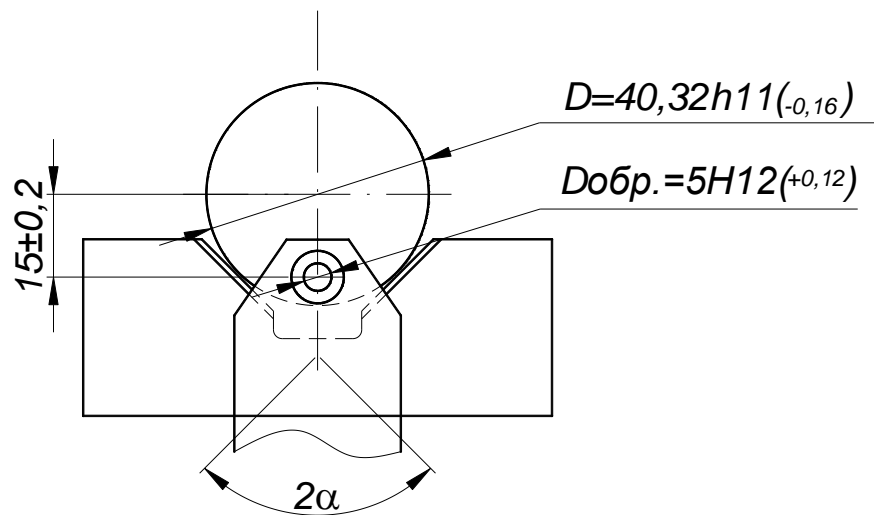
Розрахункова схема для визначення похибки базування
